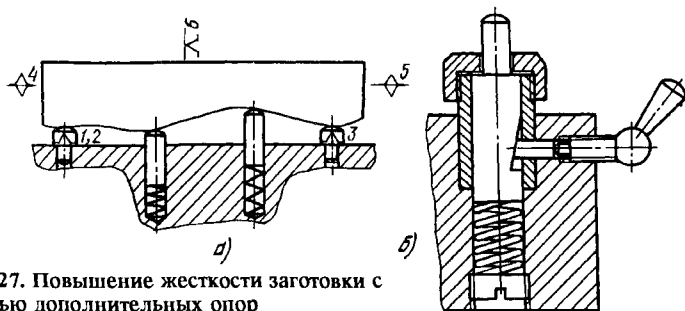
Повышение жесткости заготовки с помощью дополнительных опор
